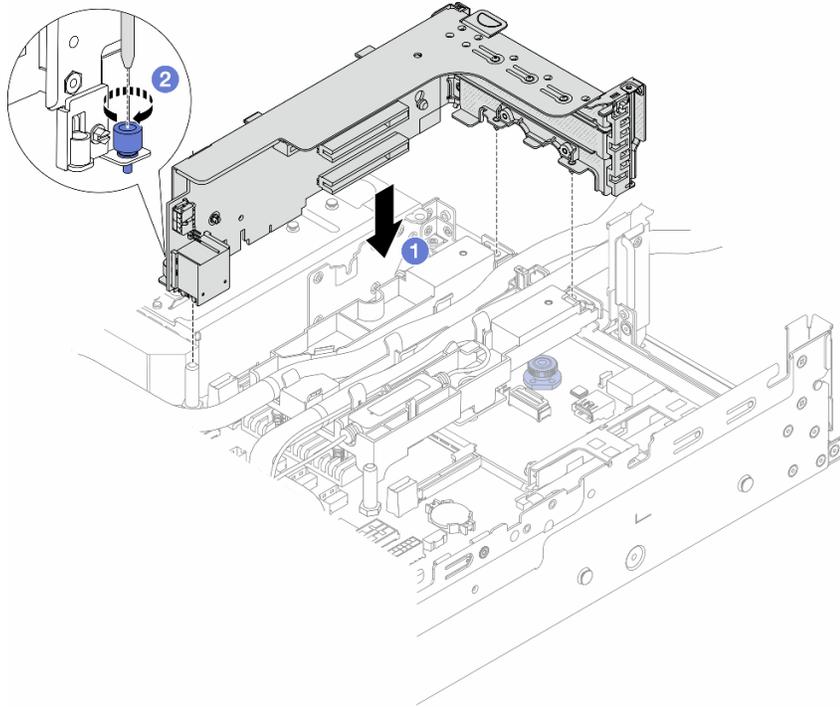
Installation du boîtier de la carte mezzanine 3FH
